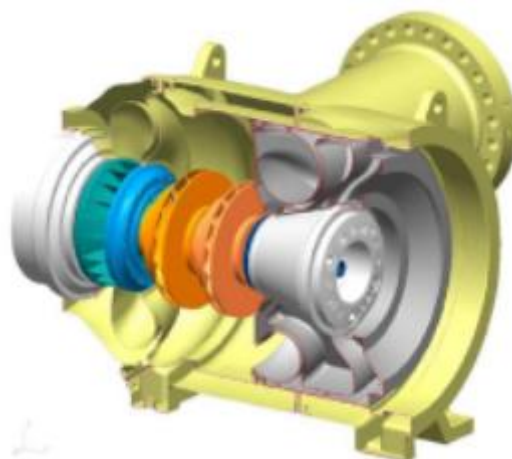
Типичный двухступенчатый центробежный компрессор, используемый в трубопроводах
